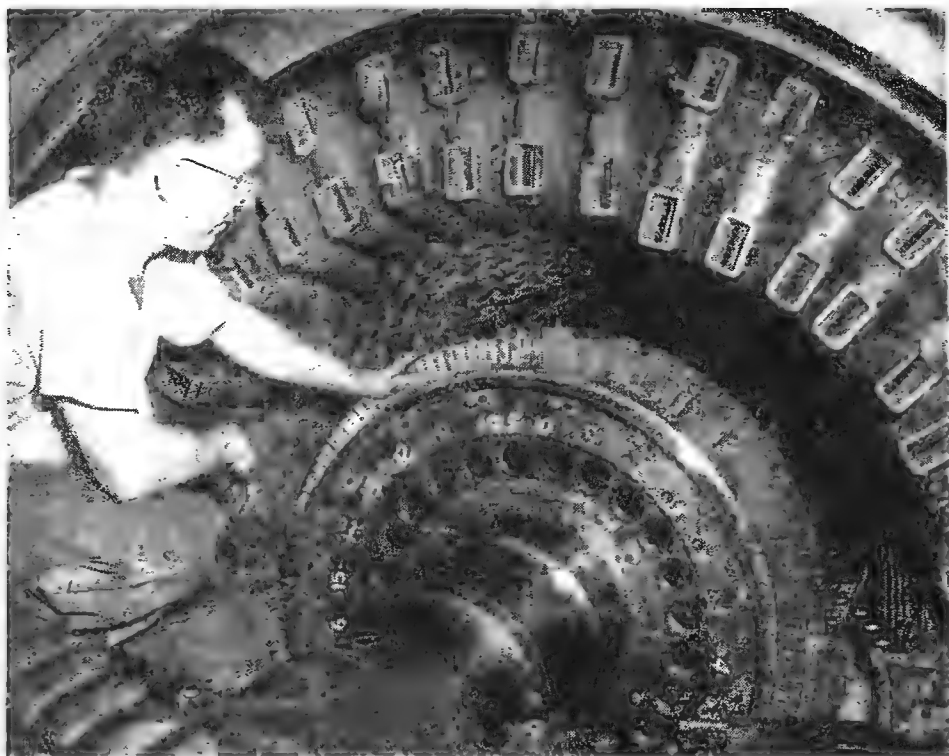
Вид лобовых частей статорной обмотки (Вестингауз Эл. К°).
